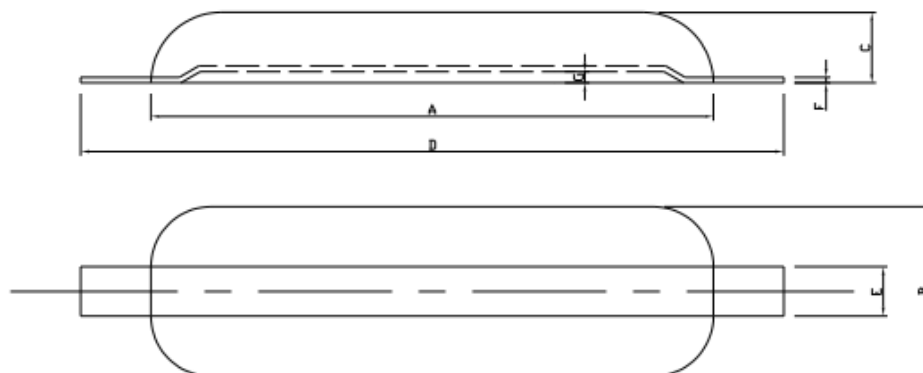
Ánodos de Zinc para cascos de buques (Del Tipo soldadura w / inserción individual)
